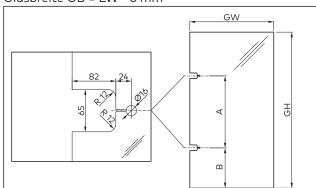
Glasbearbeitungen für die Zargenbefestigung mit eingelassener Montageplatte
